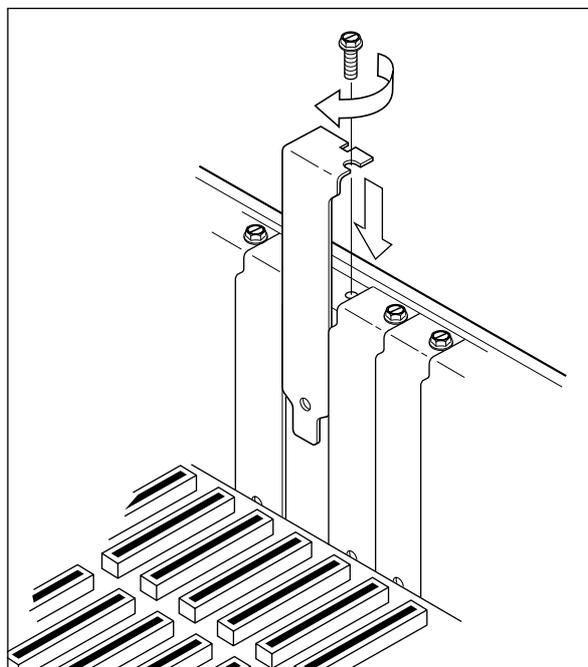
Закрытие свободного отверстия крышкой слота
